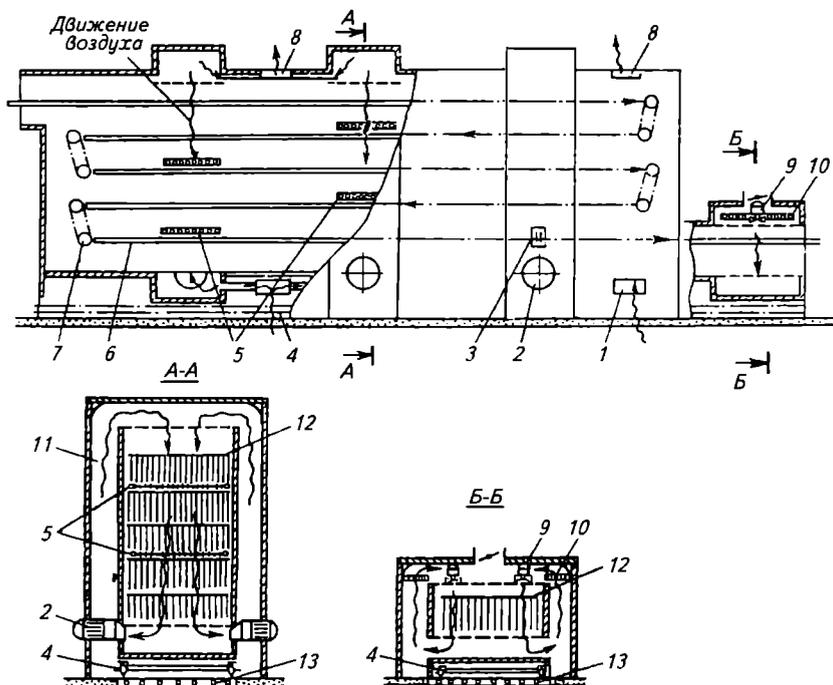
Схема окончательной сушилки Б6-ЛМВ для длинных изделий
